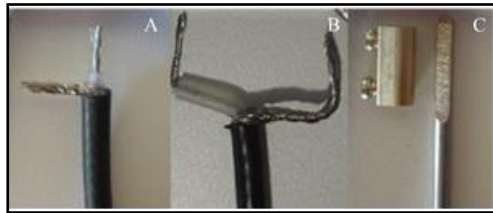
Ponta preparada para ser soldada no cabo coaxial (A), no capacitor (B) e hastes preparadas com o conector múltiplo (C)
